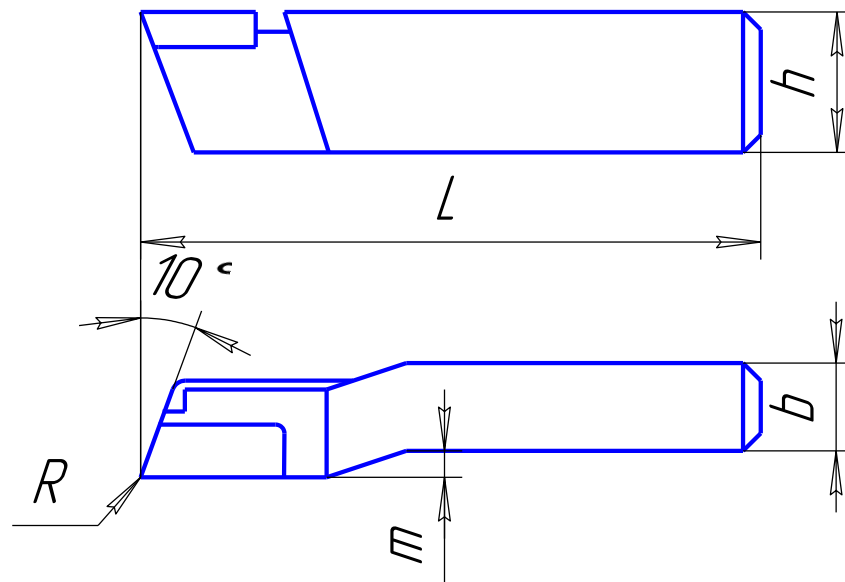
Різець токарний прохідний упорний відігнений 2103-0007 ГОСТ 18880-73.
